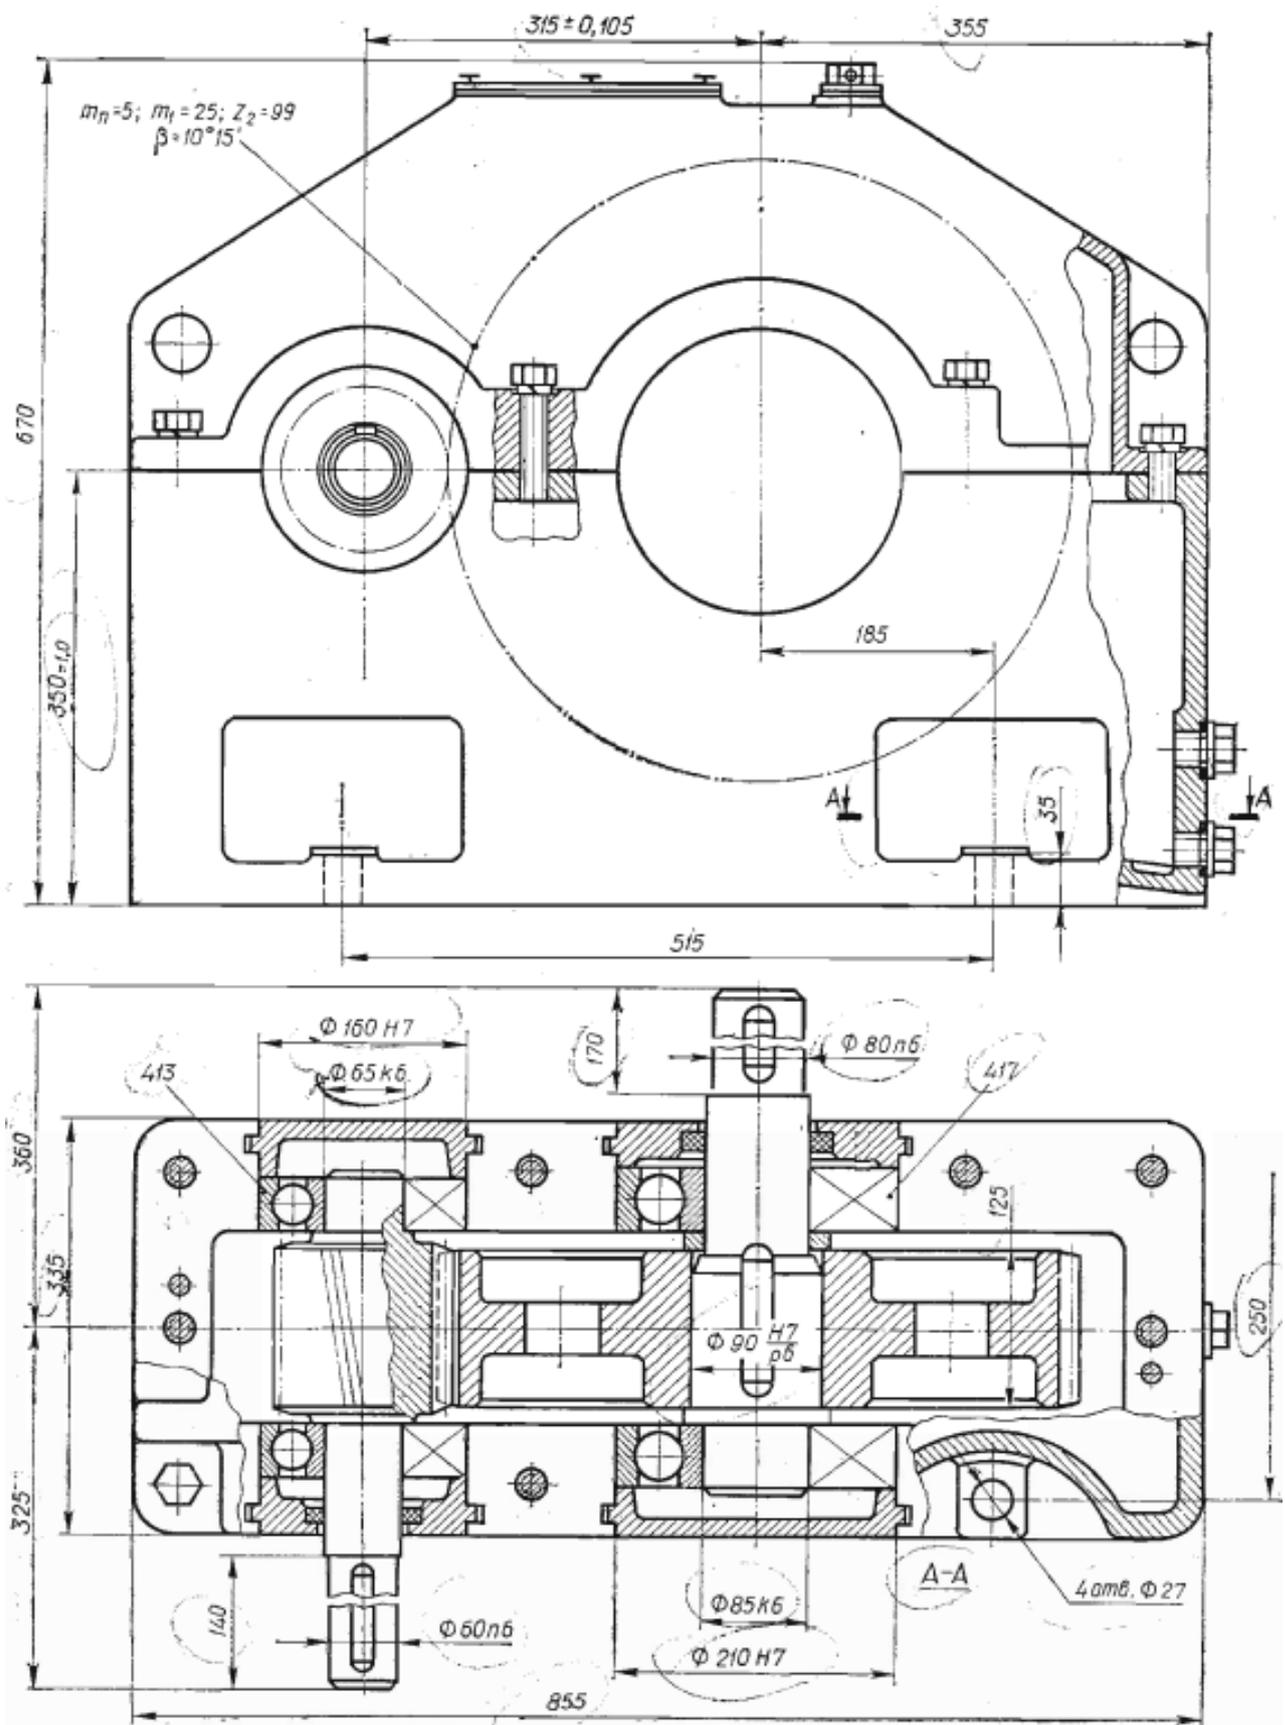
Редуктор с врезными крышками и радиальными шарикоподшипниками
